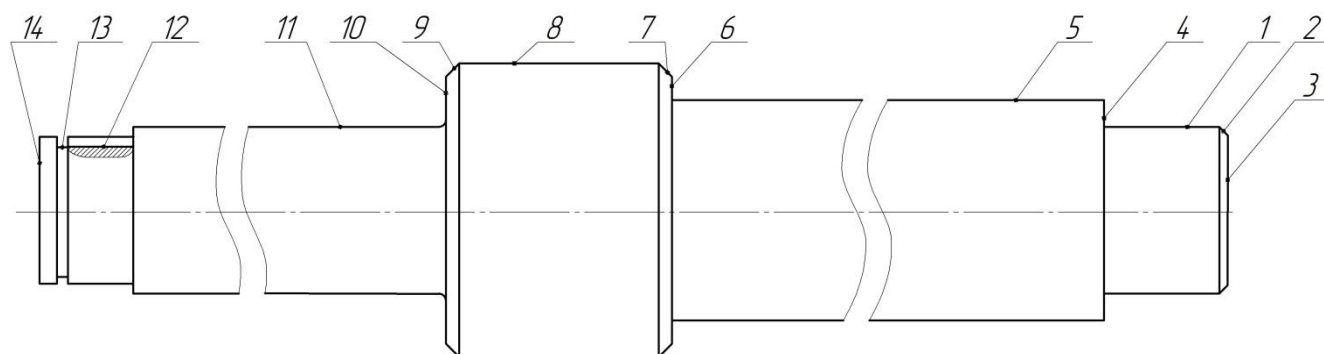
Ескіз деталі з номерами поверхонь
